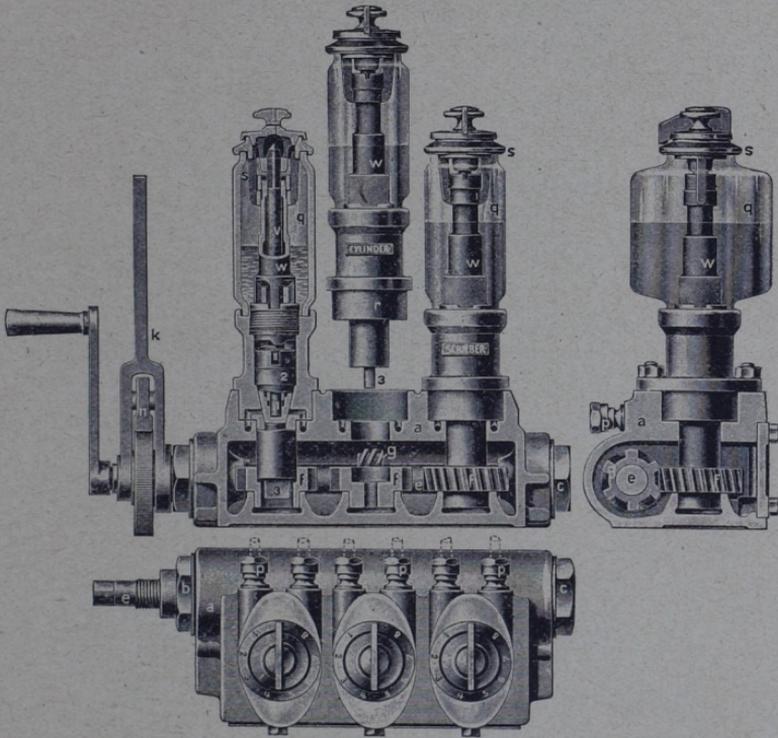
Schmierpumpe „Dicker & Werneburg“.
